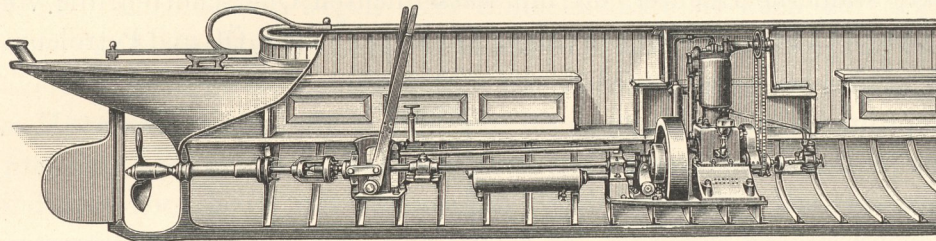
Maschinenanlage mit Otto-Motor und Meißners Umsteuerschraube.
